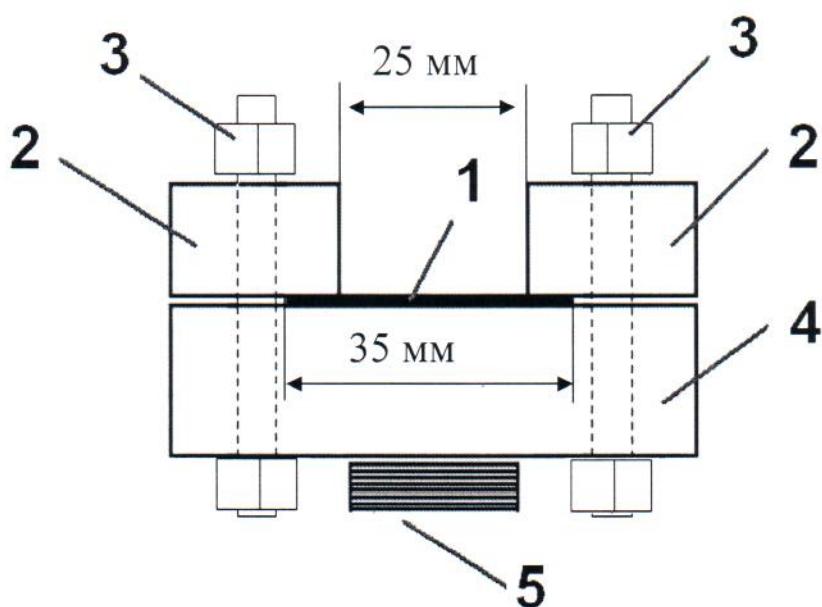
Нижняя часть приспособления для определения времени схватывания:
